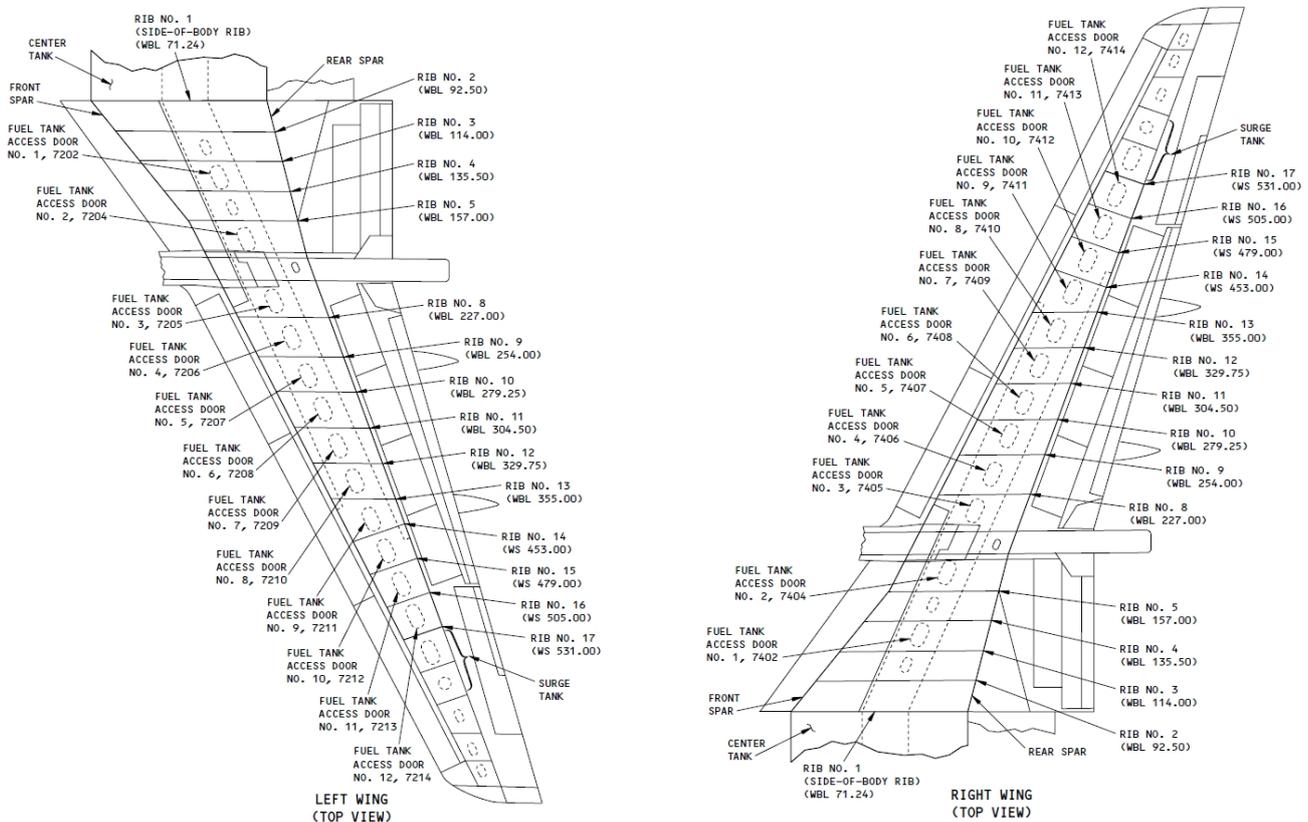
Расположение лючков доступа в топливные баки (FUEL TANK ACCESS DOOR), вид на левое и правое крыло сверху.
